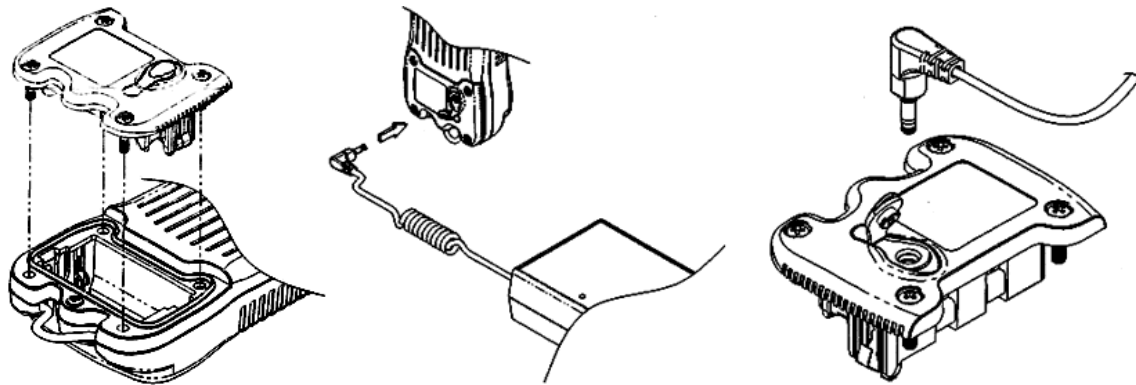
Montageablauf und Aufladen des Akku-Packs
